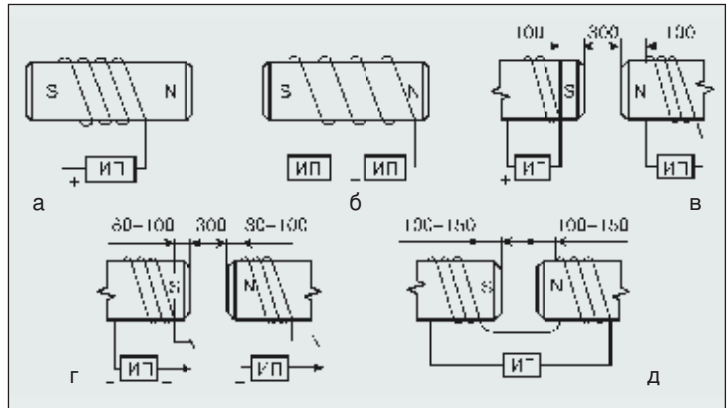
Схема проведения размагничивания постоянным током: а — по типовой методике с использованием одного сварочного преобразователя; б — по типовой методике с использованием двух последовательно соединенных сварочных преобразователей; в — размагничивание концов труб; г — по методике с разрывом магнитной цепи; д — по методике размагничивания собранных стыков труб (ИП — источник питания (сварочный преобразователь))
